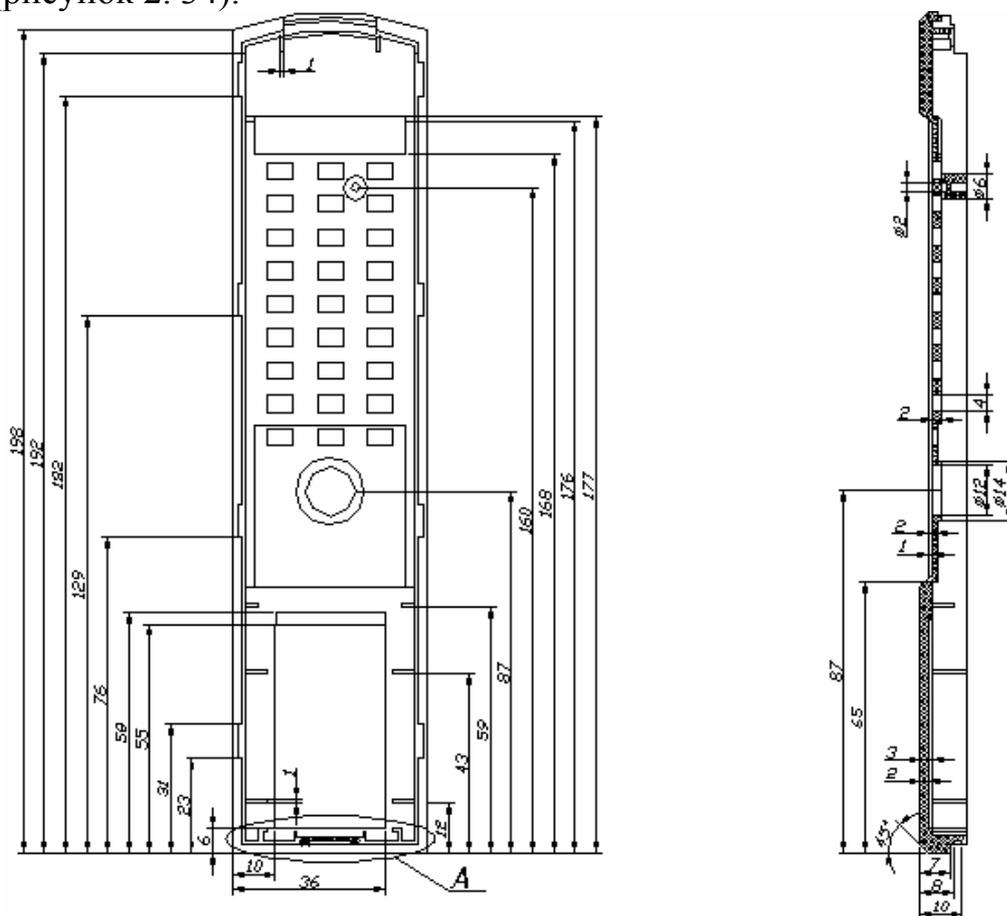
Двухмерный чертеж крышки пульта управления
